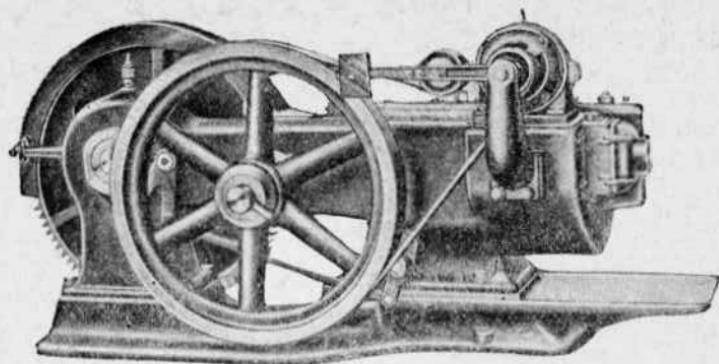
Резьбонакатный полуавтомат Кизерлинг и Альбрехт.
